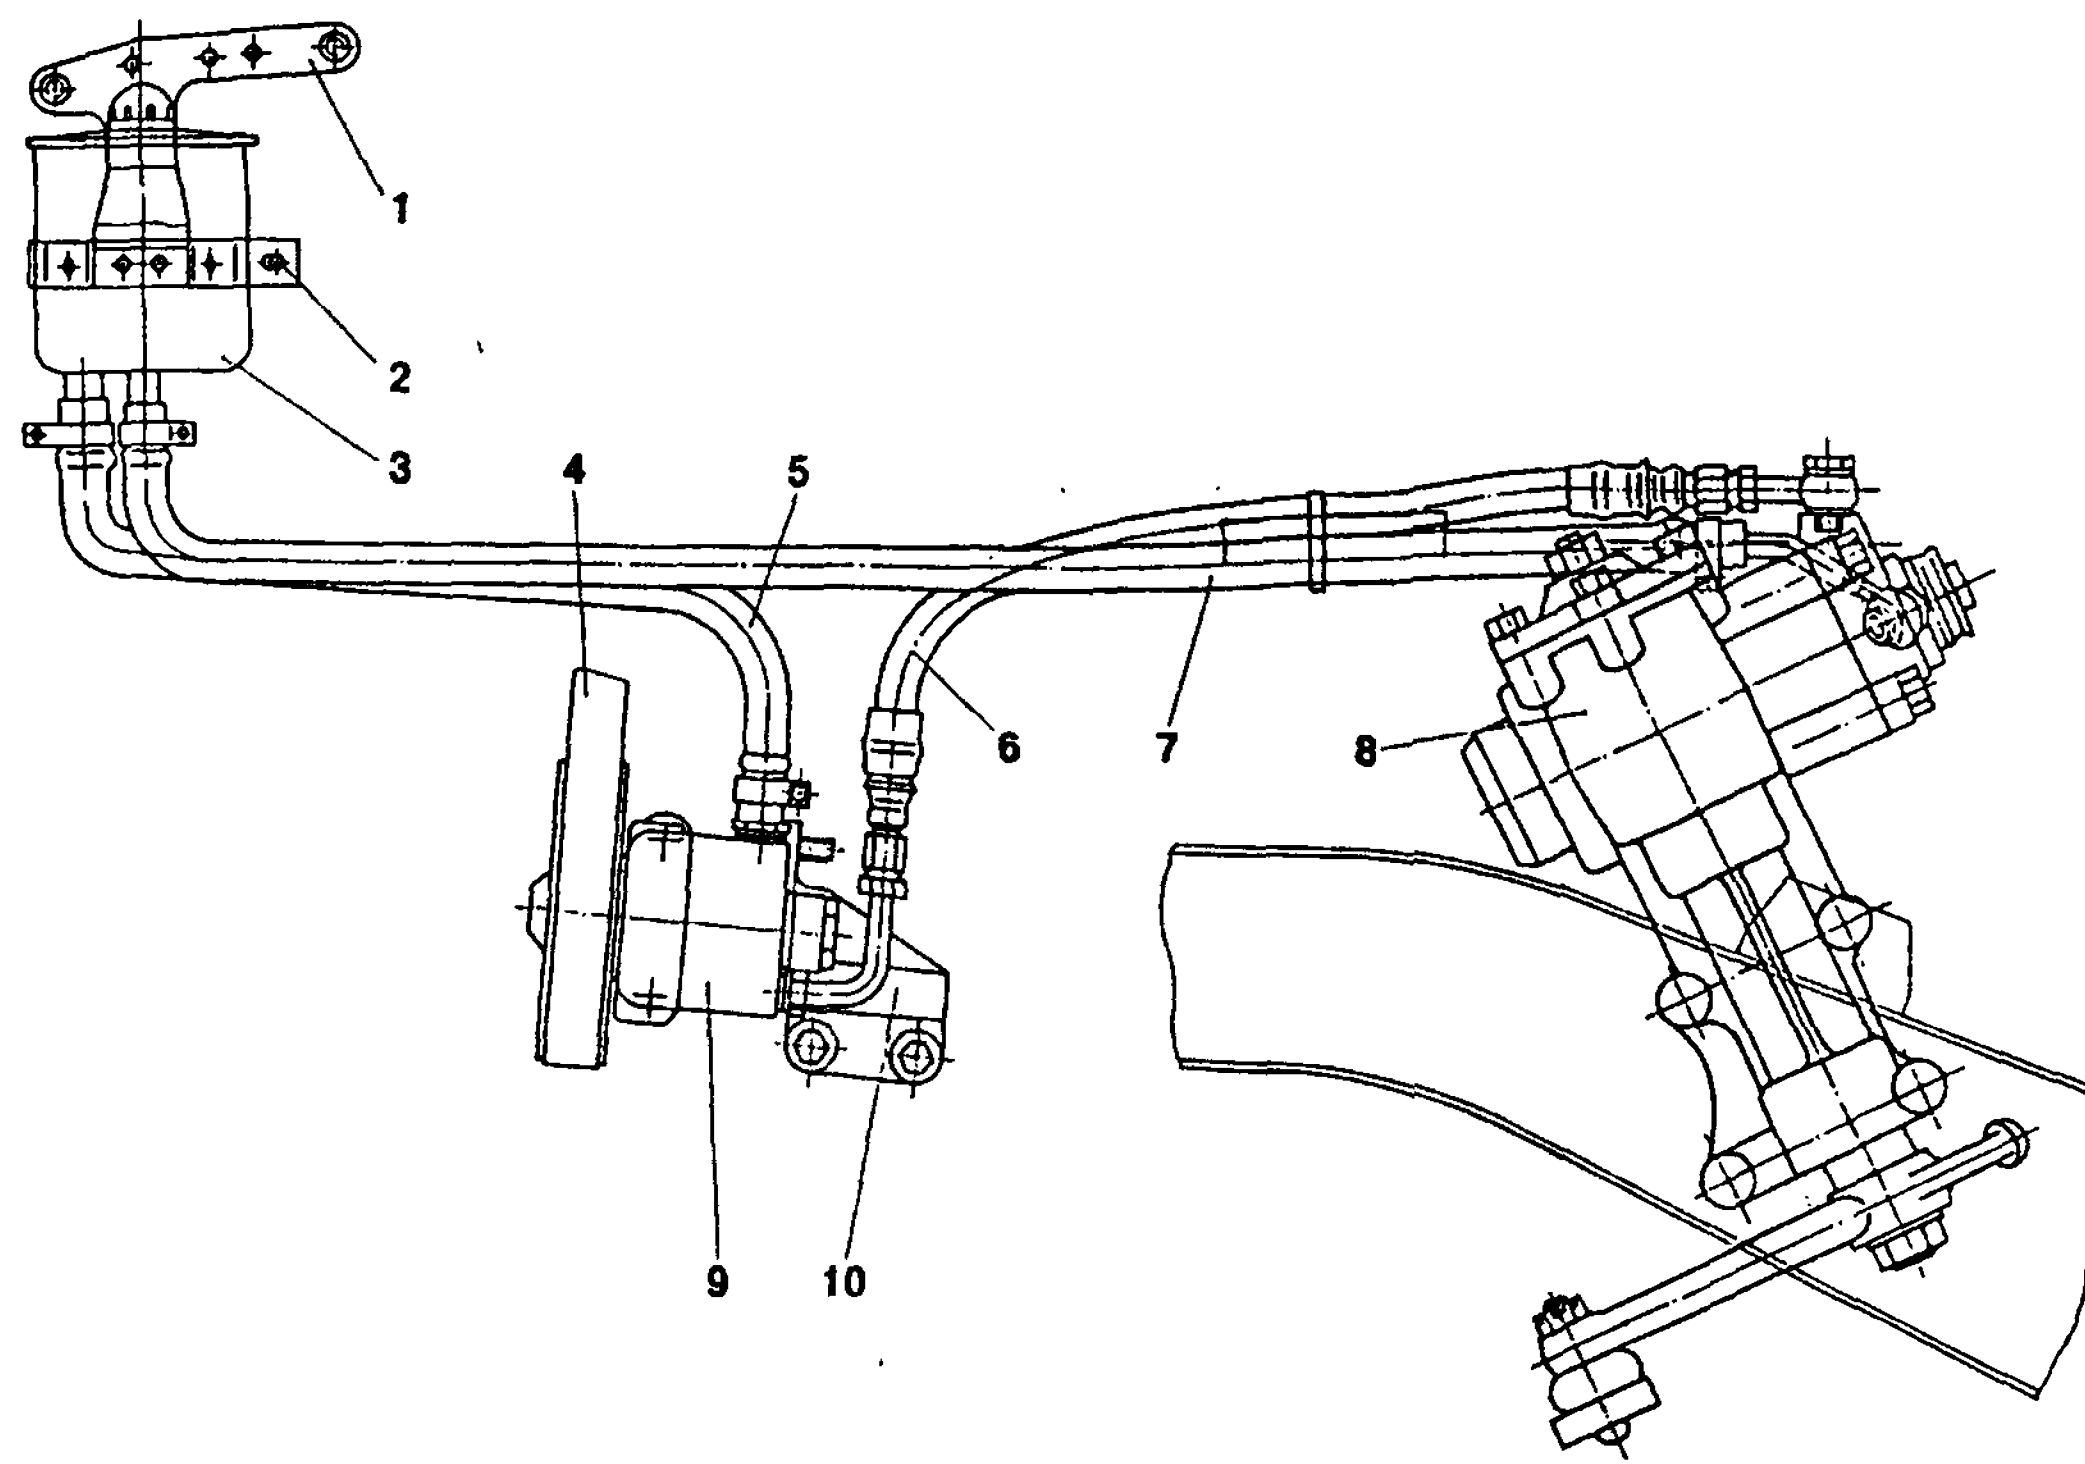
Система рулевого гидроусилителя с двигателем ЗМЗ 4062: 1 - кронштейн бачка; 2 - стяжной болт; 3 - бачок; 4 - приводной ремень; 5 - всасывающий шланг; 6 - нагнетательный шланг; 7 - сливной шланг; 8 - рулевой механизм; 9 - насос; 10 - кронштейн крепления насоса
